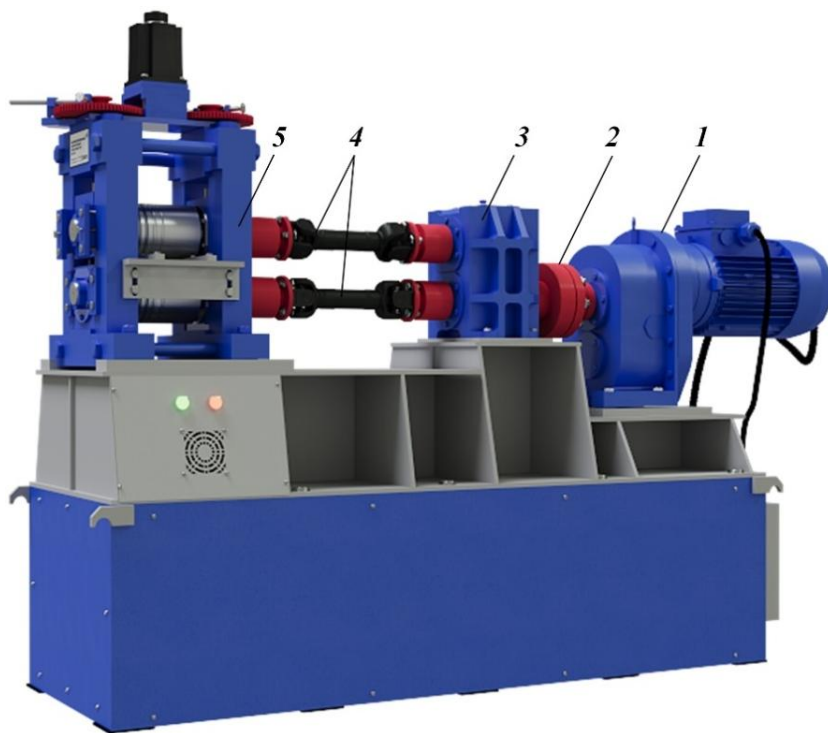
Главная линия прокатного стана ДУО-130: 1 – мотор-редуктор; 2 – муфта; 3 – шестеренная клетка; 4 – универсальный шпиндель; 5 – рабочая клетка
